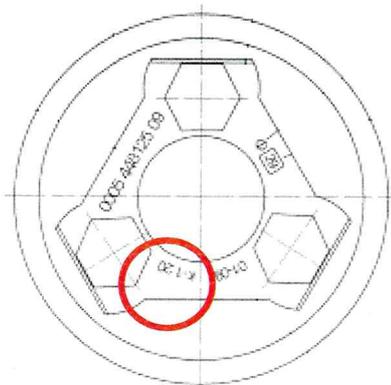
в Пример обозначения подшипника BRENCO клеймом К-1 на шайбе стопорной для колёсной пары на 3 и 4 болта торцевого крепления
